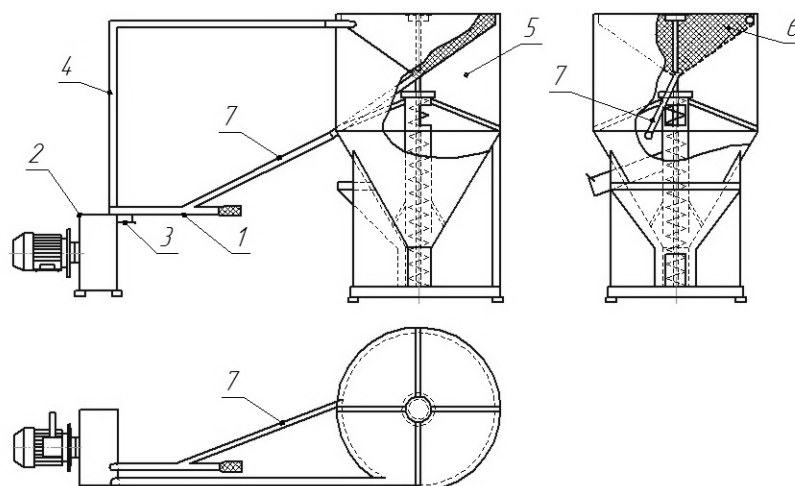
Схема предлагаемого агрегата для приготовления комбикормов:
